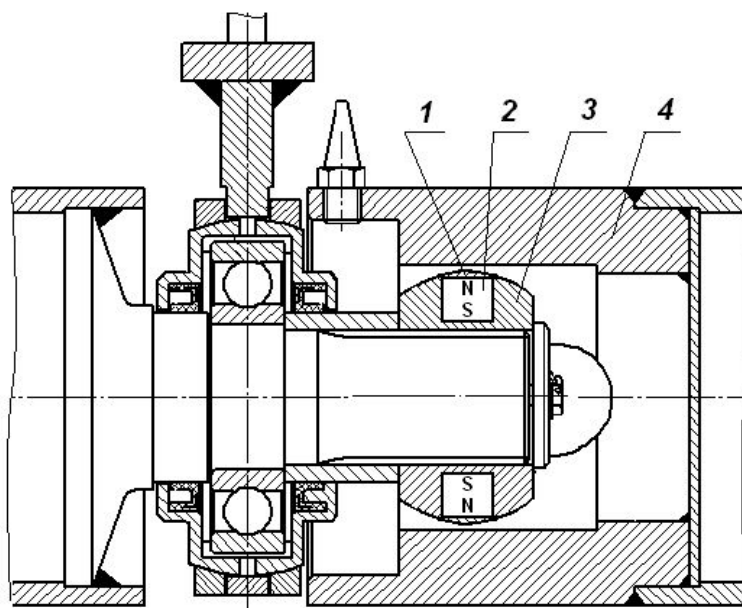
Конструкция муфты фрезерующего устройства с магнитожидкостной смазкой
